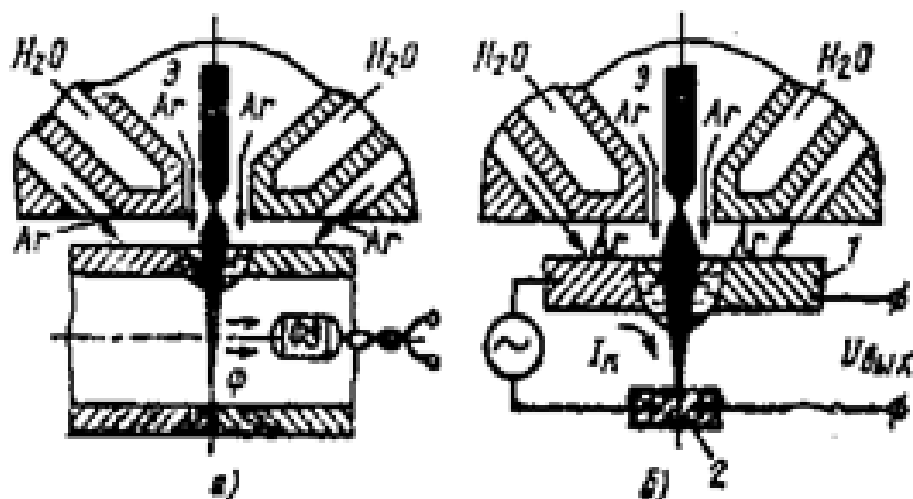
Способы контроля проплавления при плазменно-дуговой сварке
